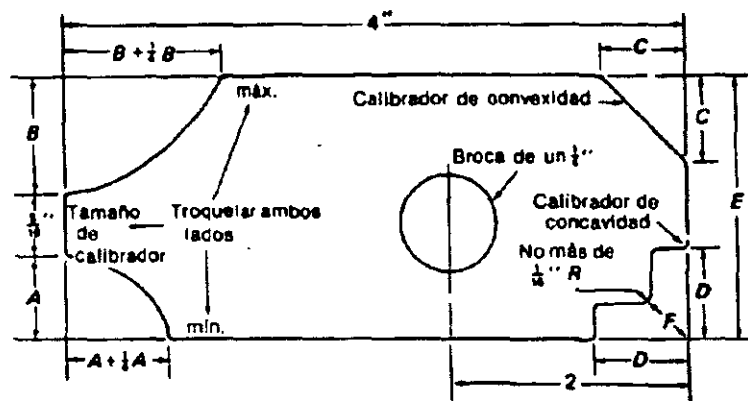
Calibrador de soldaduras de filete, únicamente
